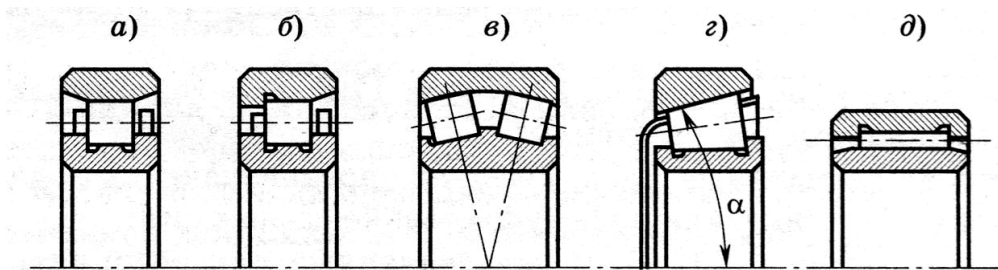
Роликовые подшипники качения: *a, б* – радиальные с короткими цилиндрическими роликами; *в* – радиальный сферический двухрядный; *г* – конический однорядный; *д* – игольчатый
